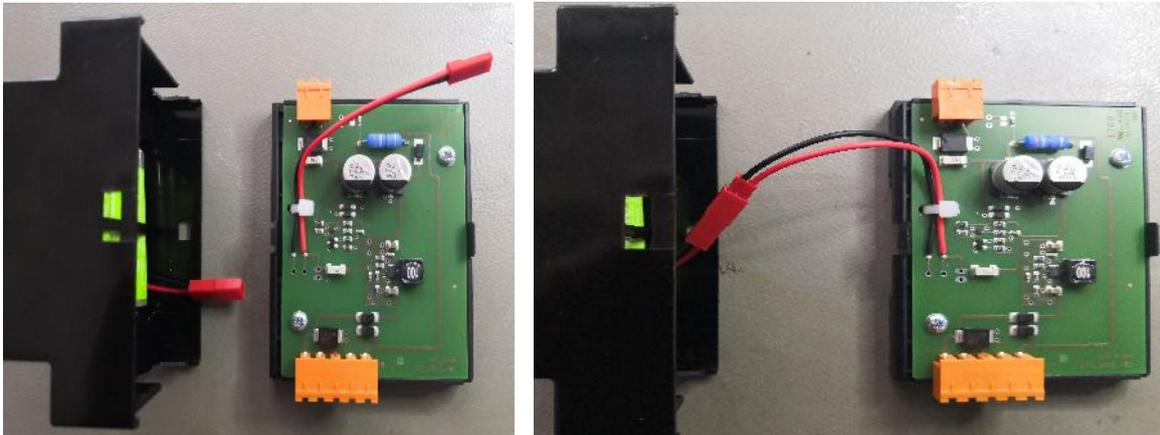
Links: Buchse auf Akkuseite - Stecker auf Printseite;
